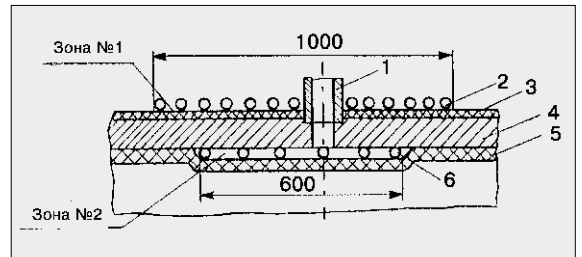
Схема установки электронагревателей в зонах нагрева: 1 — штуцер пароводящей трубы размером 133×18 мм; 2 — индуктор в зоне нагрева №1; 3 — асбестовая теплоизоляция; 4 — стенка барабана; 5 — теплоизоляция базальтовыми матами; 6 — электронагреватель КЭН–4–3М в зоне нагрева
